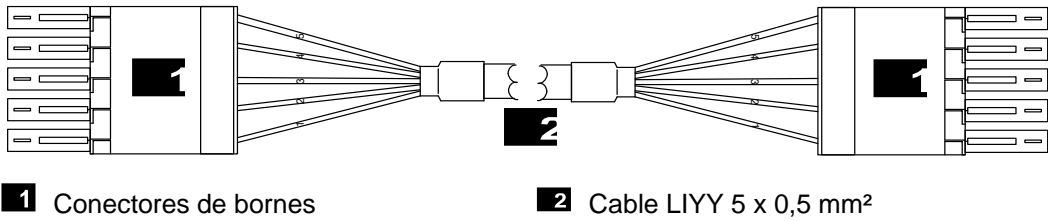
Cable del kit de cables de sistema X-CA 004 01
